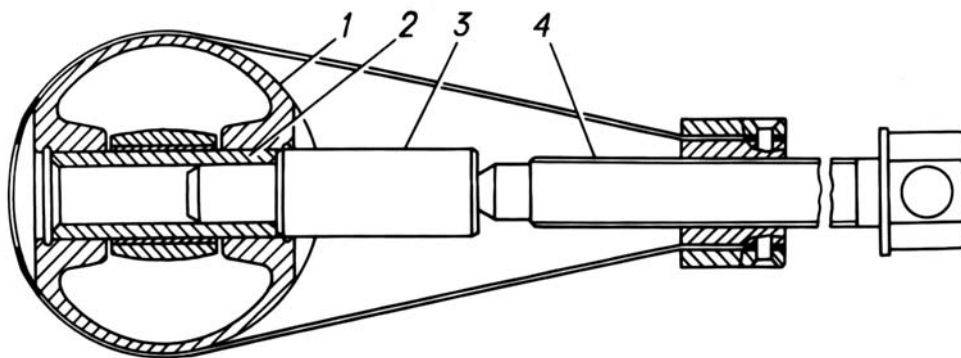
Выпрессовка поршневого пальца из поршня при помощи приспособления:
